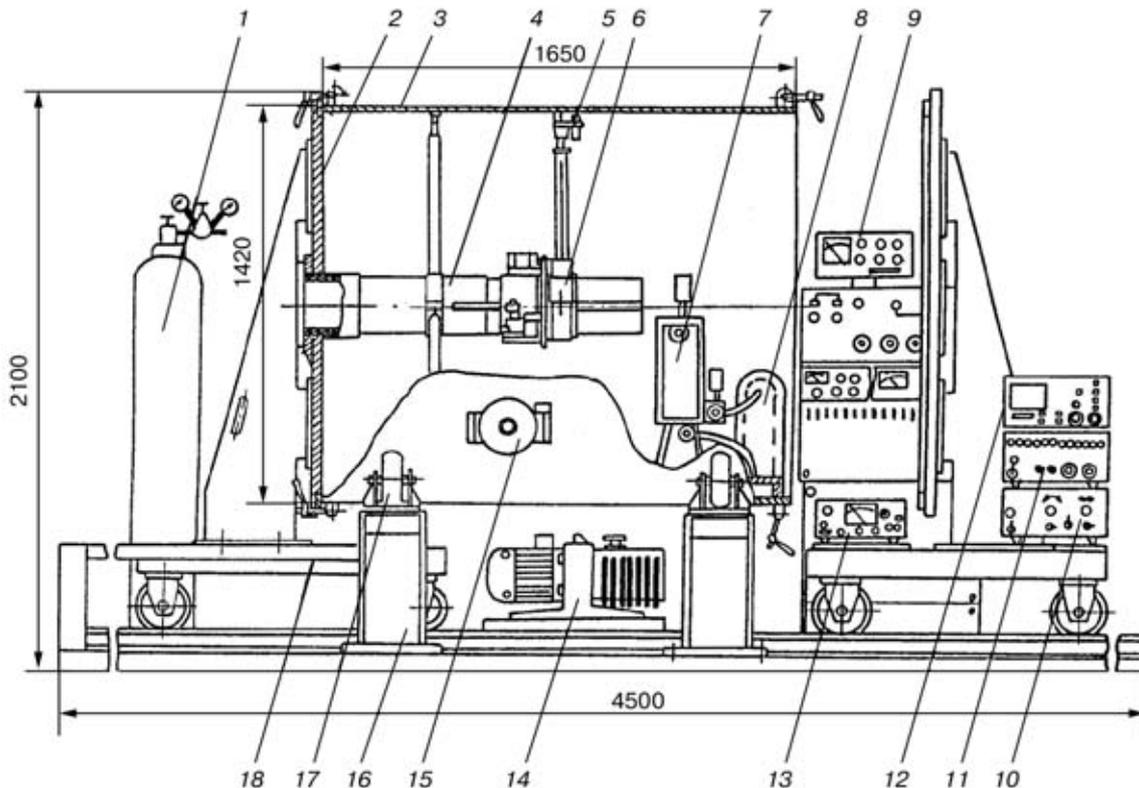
Лабораторный стенд Об-2266 для испытания методов и средств контроля герметичности сварных соединений многослойных труб большого диаметра и других крупногабаритных изделий (обозначения см. в тексте)
